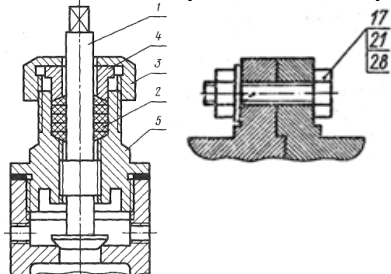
Расположение номеров позиций для группы деталей
